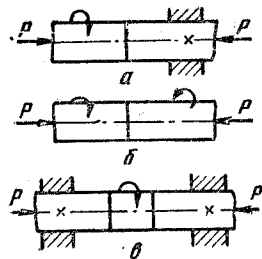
Принципиальные схемы сварки трением с использованием вращения одной детали (а), двух деталей (б) и вставки (в)
